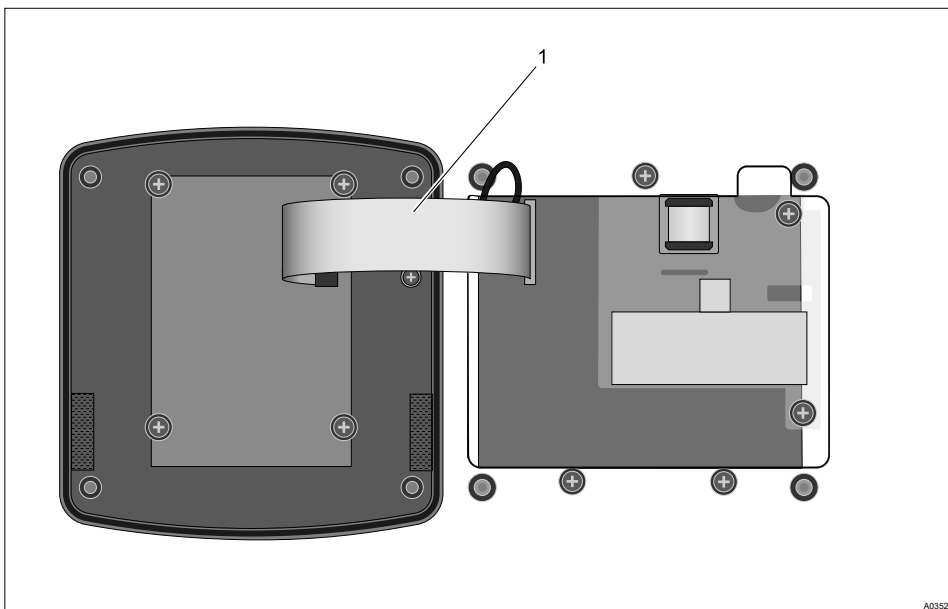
Flachbandkabel in Sockel stecken und verriegeln
